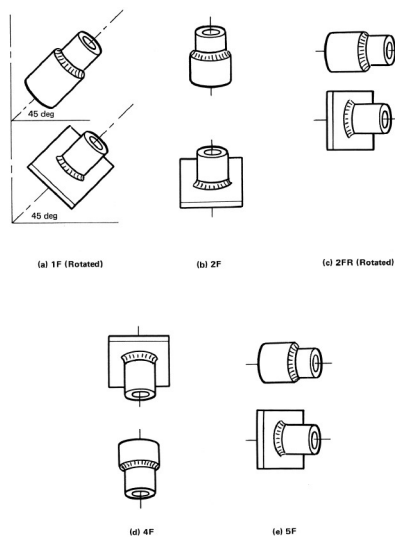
POSICIONES PARA SOLDADURA DE FILETE EN TUBERÍA.
